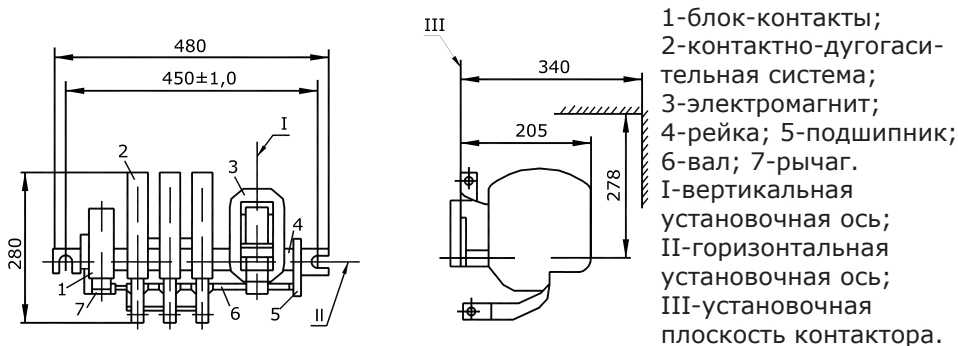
Габаритные и установочные размеры двух- и трехполюсных контакторов типа КТ, КТП-6000 на ток 400А исполнения 2.
